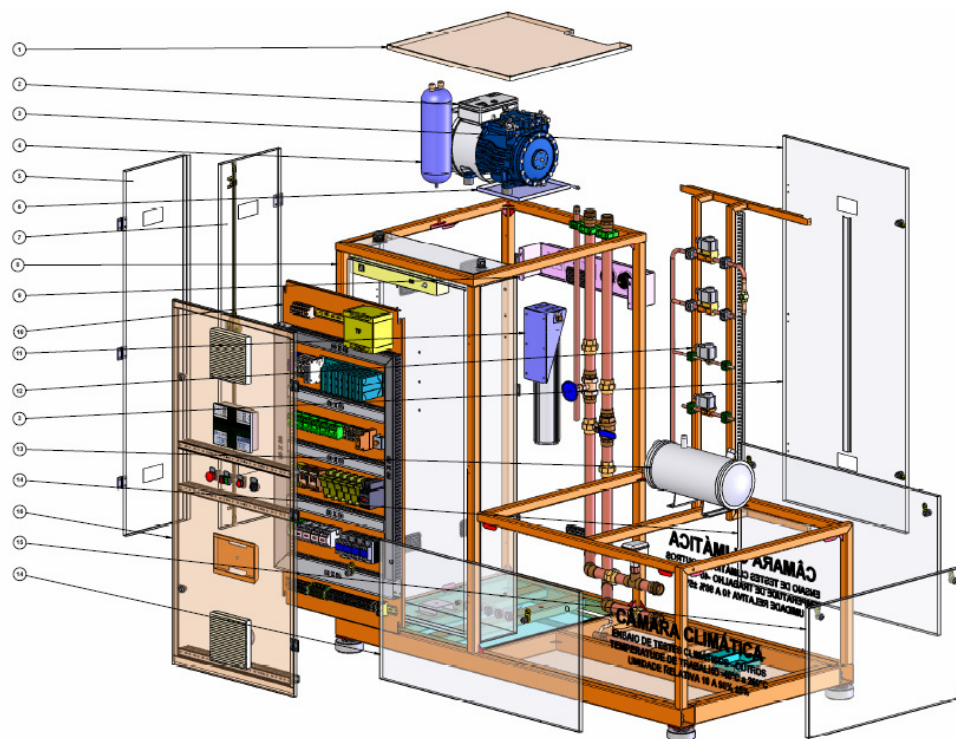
Exemplo de Desenho Dimensional Casa de Máquina e Painel de Controle
